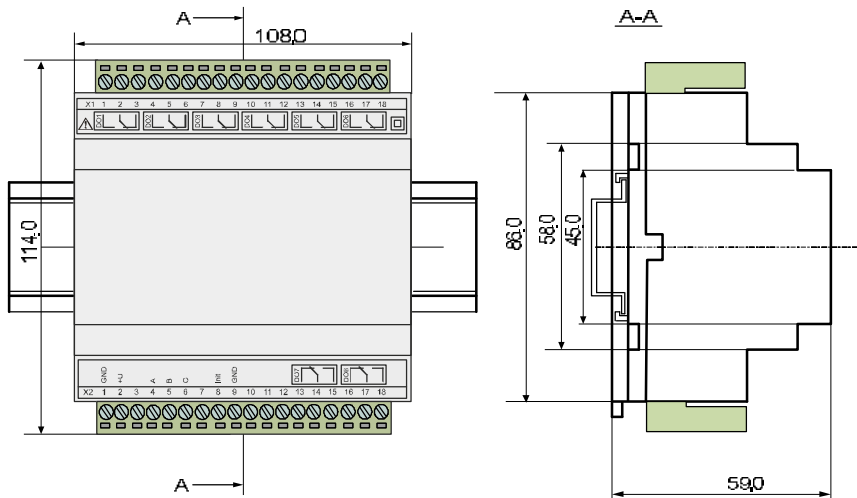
Габаритные и присоединительные размеры модуля
